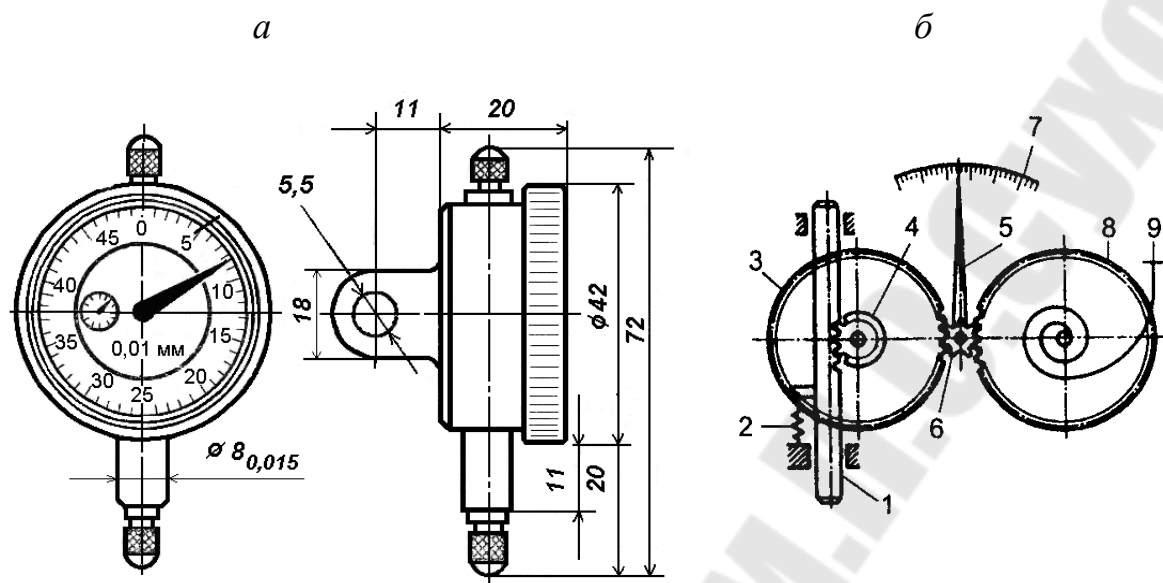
Индикатор часового типа: а) общий вид; б) кинематическая схема индикатора: 1 – зубчатая рейка стержня; 2 – пружина; 3 – шестерня; 4 – реечный триб; 5 – стрелка; 6 – стрелочный триб; 7 – шкала; 8 – зубчатое колесо; 9 – пружинный волосок.
